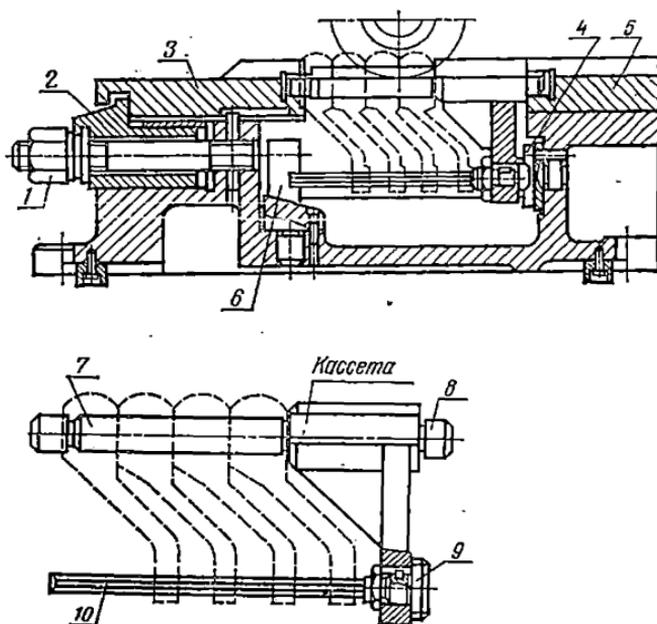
Многоместное приспособление для фрезерования пазов в рычагах:
